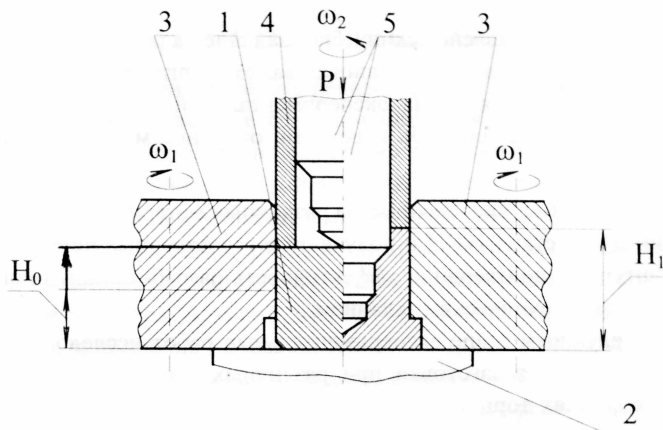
Схема изготовления ступенчатых деталей с внутренней полостью.
